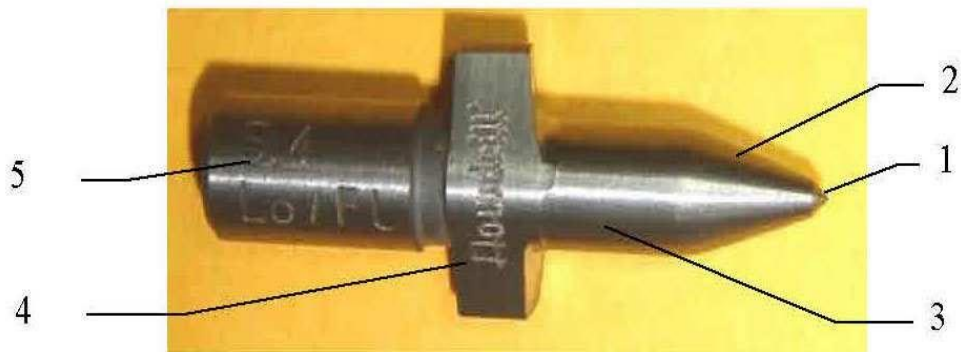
Перфоратор FlowDrill: 1 – конічна (центруюча) робоча частина;
